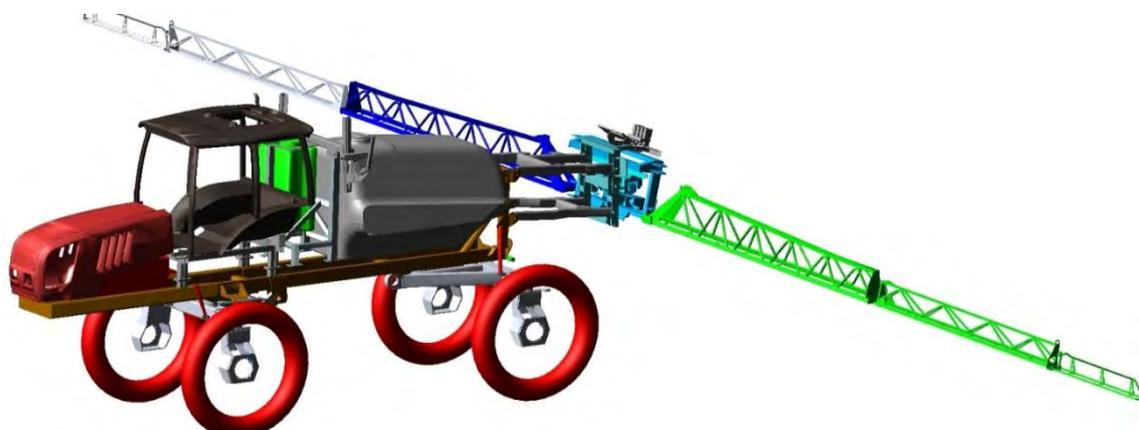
Виртуальная модель самоходного опрыскивателя с разложенными штангами
